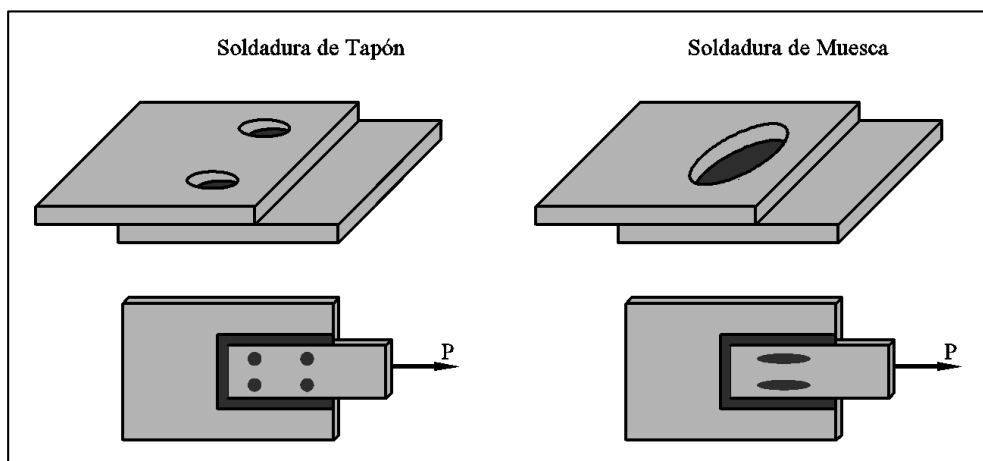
Soldadura de Tapón y de Muesca.
